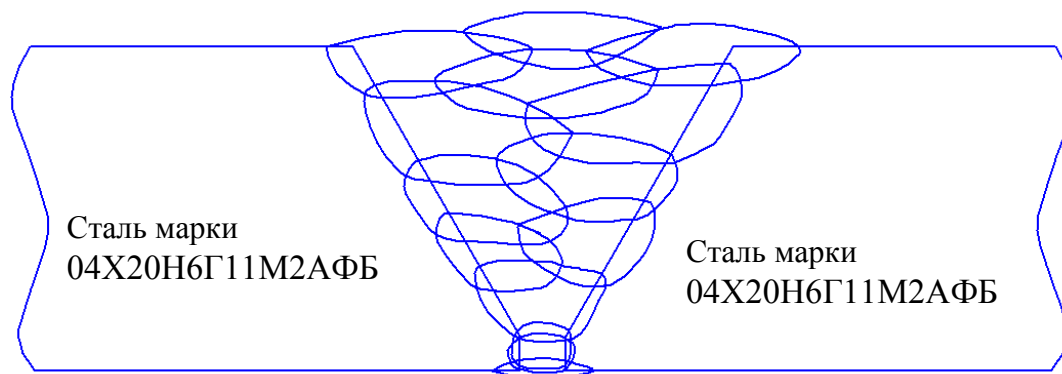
Схема раскладки валиков по сечению металла шва V-образного сварного соединения сталей 04X20H6Г11M2АФБ, выполненного присадочной проволокой ЭП-263Ш
